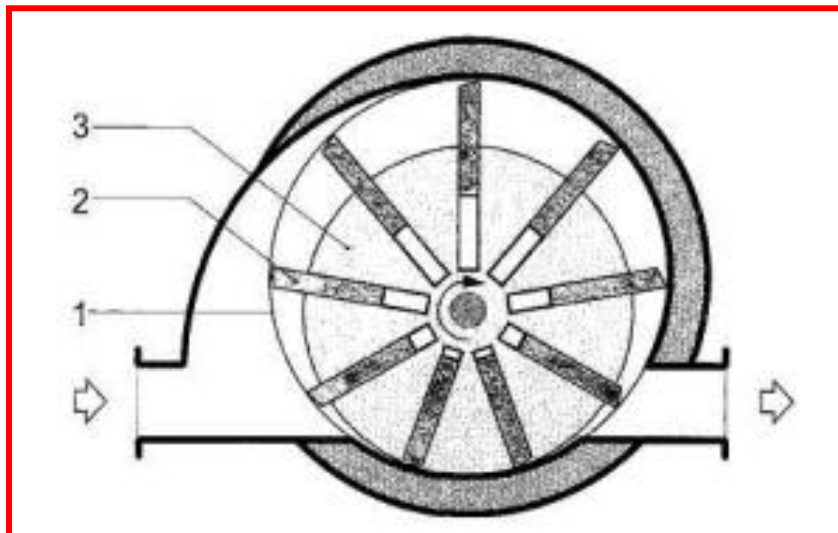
Пластинчатый (шиберный) компрессор: 1 – цилиндрический статор (корпус); 2 – пластина; 3 – ротор
